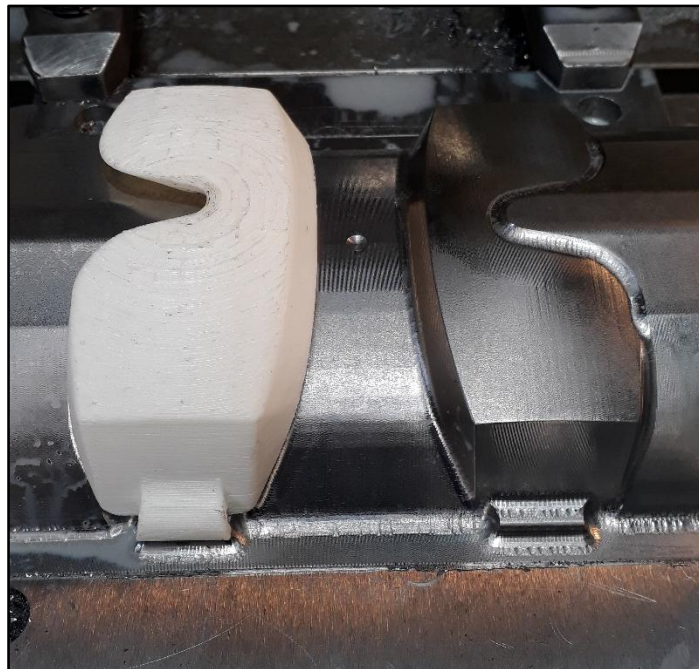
, desbaste, taladrados molde macho gafas. Fuente: Autor.
